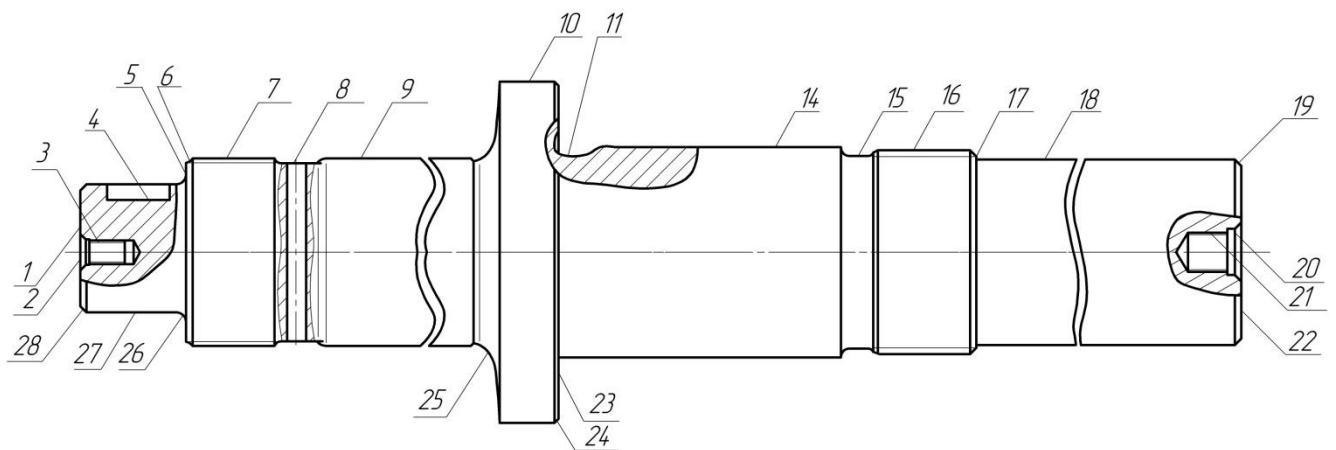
Нумерація поверхонь деталі Вал
